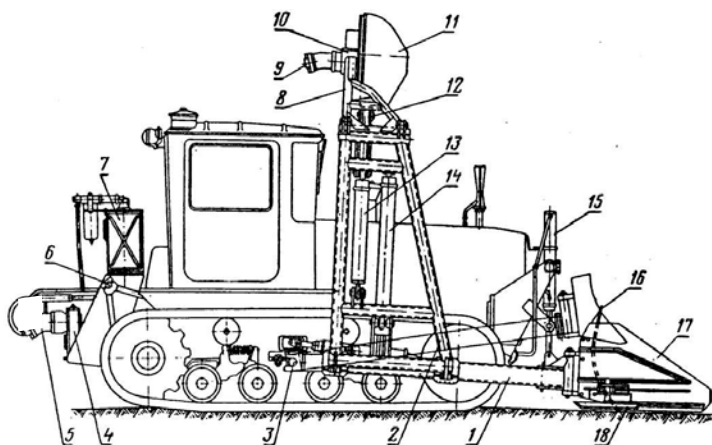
Каналоочиститель МР-14 с фрезерным рабочим органом: 1 – толкающая рама; 2 – рама; 3 – упряжный шарнир; 4 – редуктор; 5 – насос; 6 – трактор; 7 – бак; 8 – рукоять; 9 – гидромотор; 10 – редуктор; 11 – фрезерный рабочий орган; 12, 13, 14, 15 – гидроцилиндры; 16 – отвал; 17 – уширители; 18 – опорная лыжа
